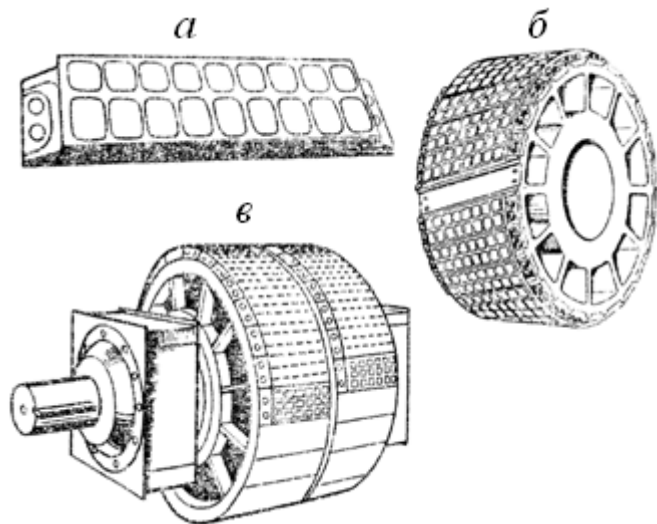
Сегмент (а), корпуса вала с сегментами (б), валок с корпусами подшипников (в)
